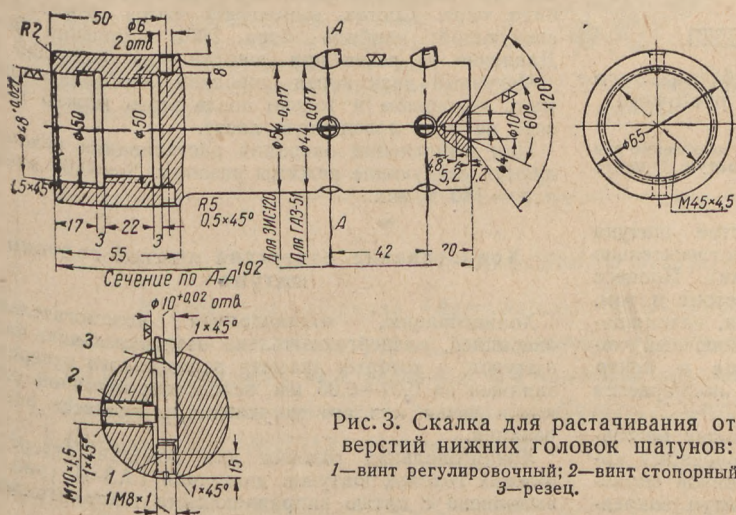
Скалка для растачивания отверстий нижних головок шатунов: 1 — винт регулировочный; 2 — винт стопорный; 3 — резец.
